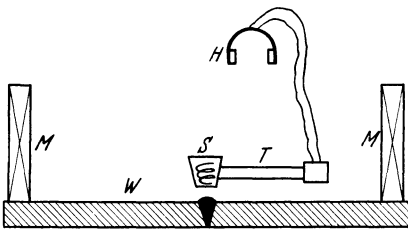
Schema des IG-Schweißnahtprüfers.
